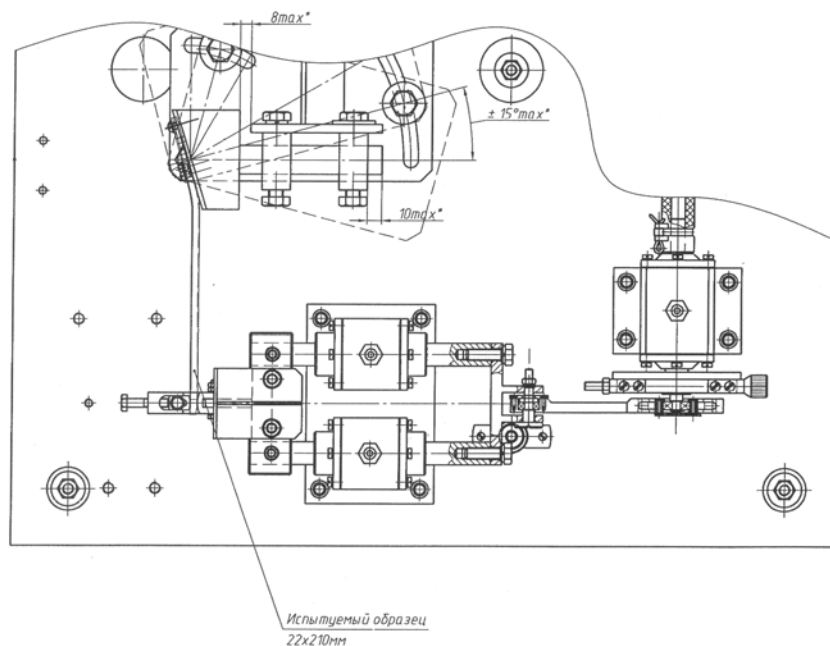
Общий вид стенда для усталостных испытаний образцов медиальных накладных пластин (вид сверху)
